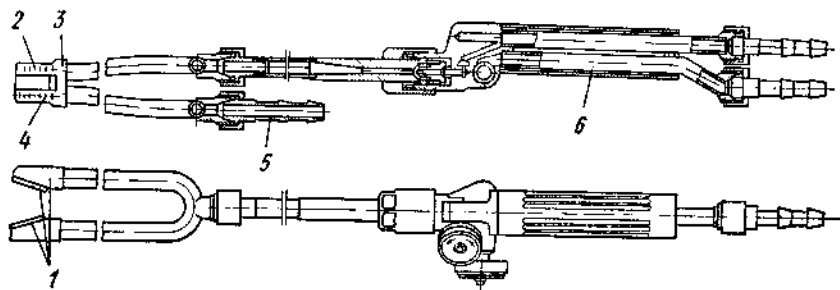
Горелка с наконечником для заковки зубьев шестерен:
